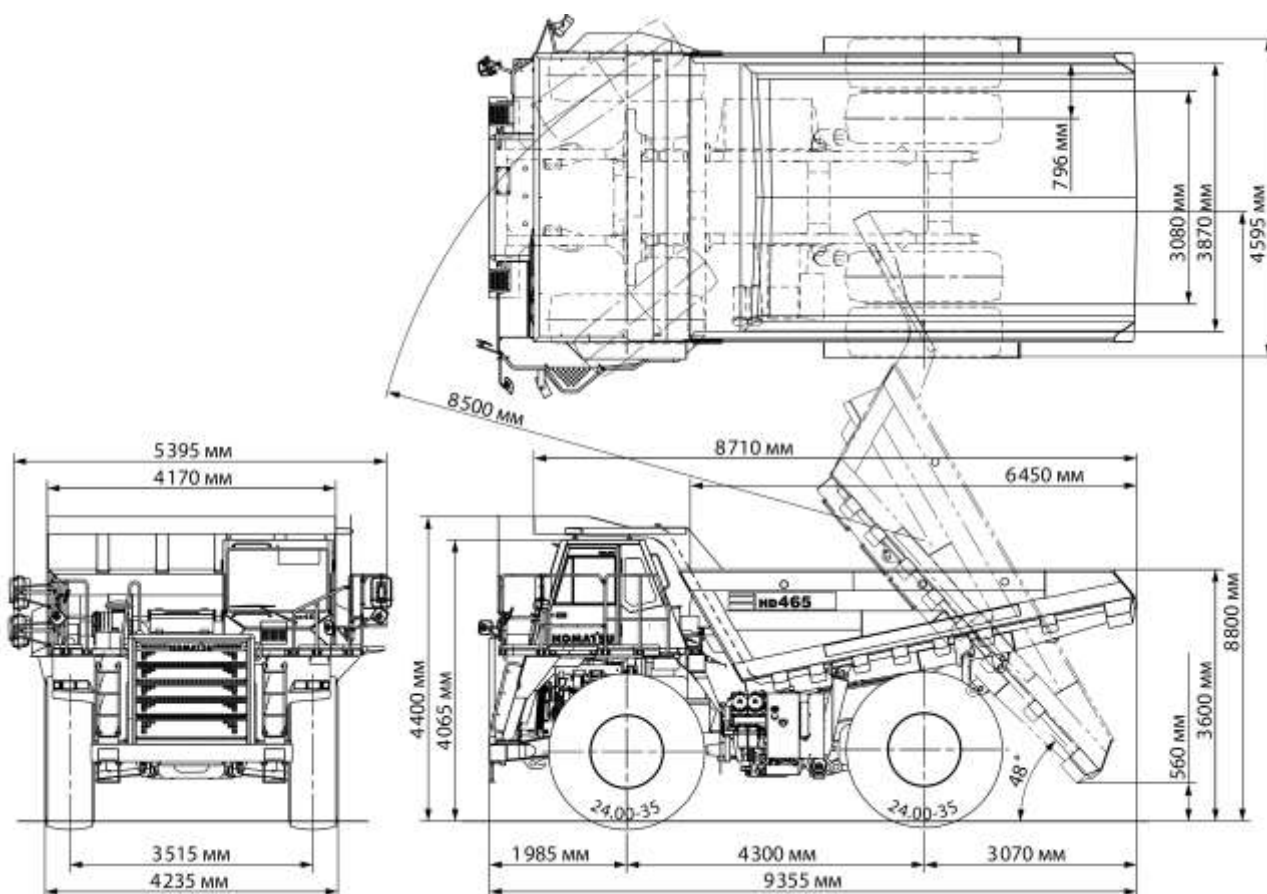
Габаритные размеры самосвала Komatsu HD465
